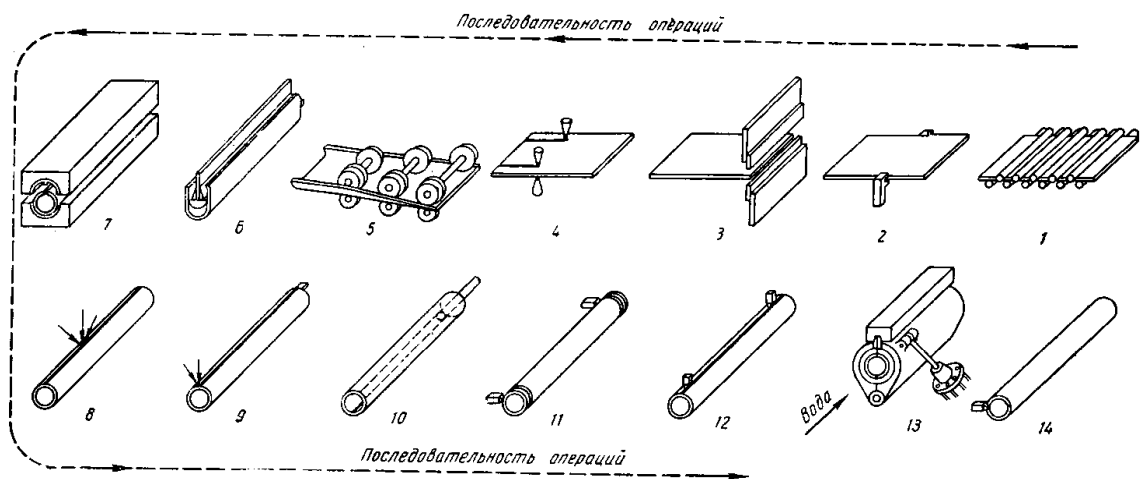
Схема технологического процесса производства прямошовных труб дуговой сваркой
